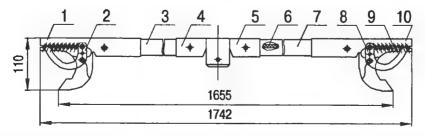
Шунт для испытания рельсовых цепей ШУ-01М-00
